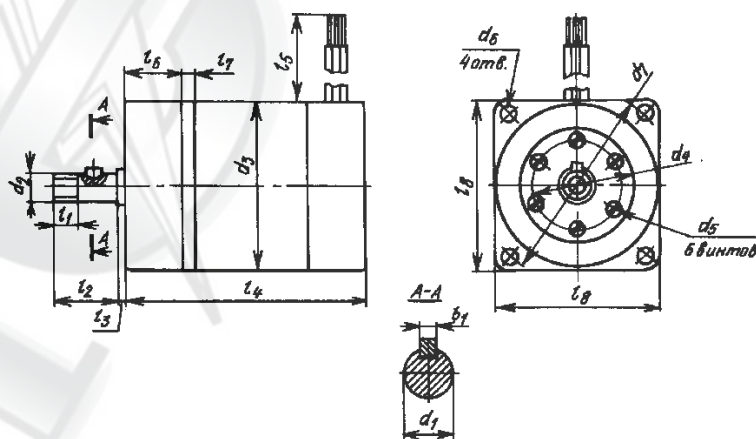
Габаритные и присоединительные размеры двигателей (исполнение фланцевое с одним свободным концом вала)
